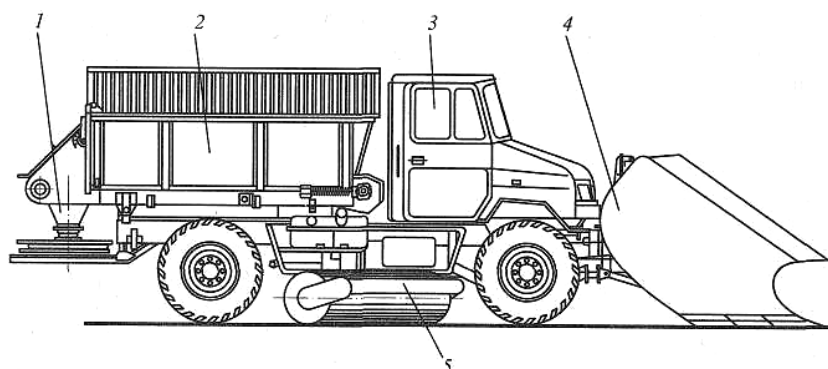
Снегоочиститель плужный, с подметальным оборудованием и
